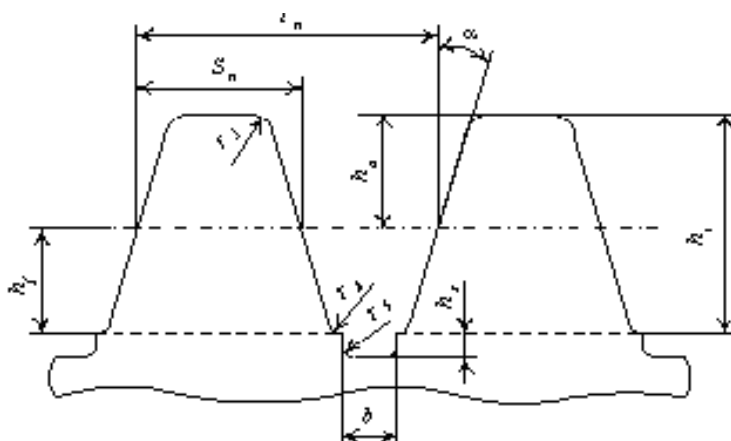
Розміри зубця фрези в осьовому перетині
